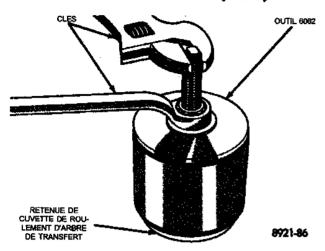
Dépose de cuvette de pignon d'arbre de transfert
